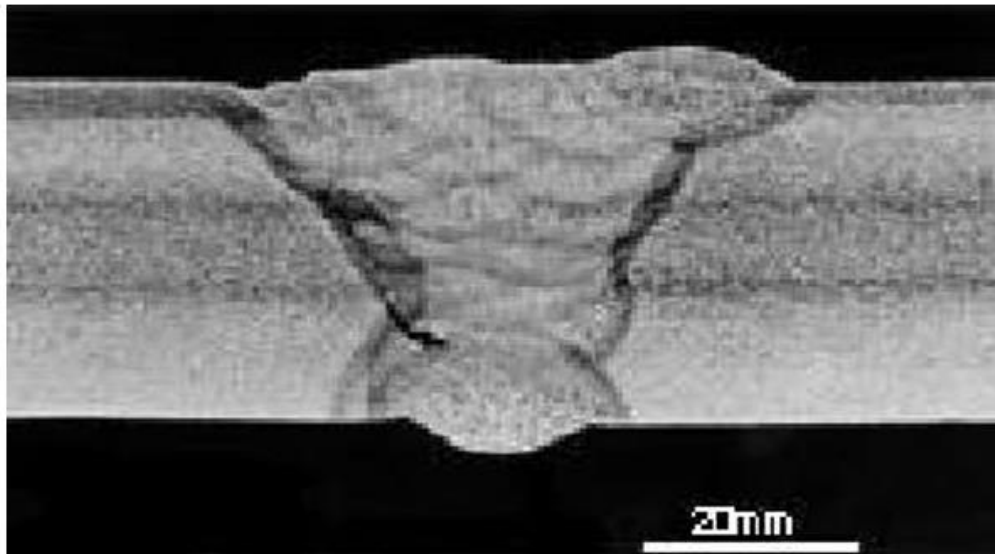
Manque de fusion dans le flanc de la soudure.
